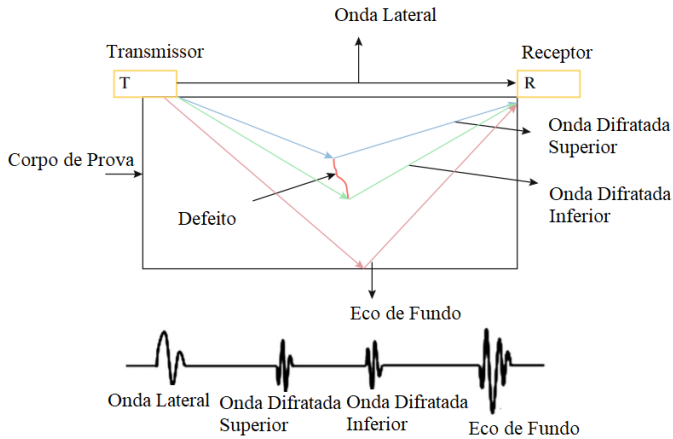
Técnica de inspeção *ToFD*, adaptado de [5].
